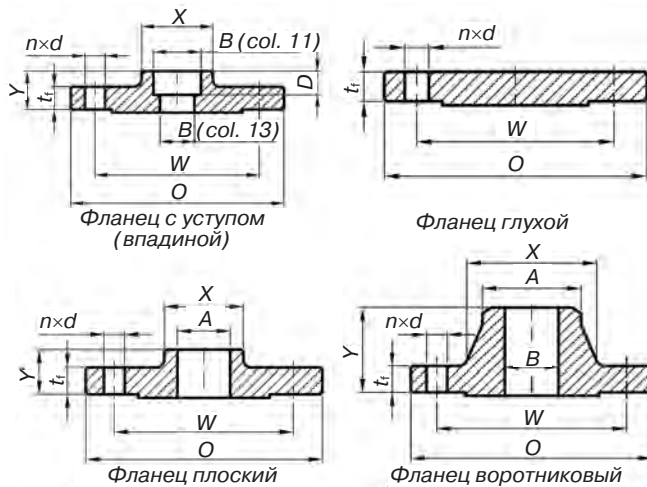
Габаритные чертежи фланцев по стандарту ASME/ANSI
